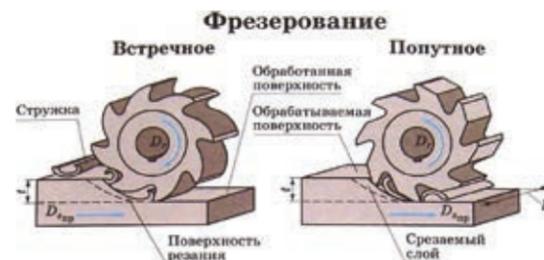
Схемы встречного и попутного фрезерования заготовок
